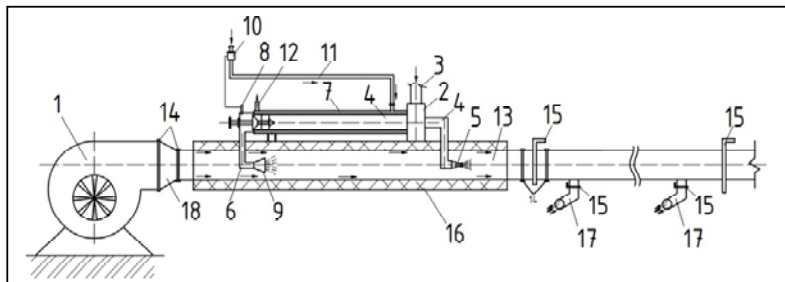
Загальний вид охолоджувальної установки «Клімат»: 1 - від-центровий вентилятор; 2 - пневматичний вихровий пристрій; 3 - патрубок для підведення стисненого повітря; 4 - патрубок холодного повітря; 5 - сопло Лавалля; 6 - патрубок гарячого повітря; 7 - водяна охолоджувальна рубашка; 8 - датчик температури повітря; 9 - дифузор; 10 - електроклапан; 11 - гідравлічна система; 12 - зливний патрубок; 13 - вентиляційний трубопровід; 14 - фланцеве з'єднання; 15 - шибери кількісної регуляції повітря; 16 - абсорбційний глушник трубчастого типу; 17 - поворотні душіруючі патрубки ПДП-100
